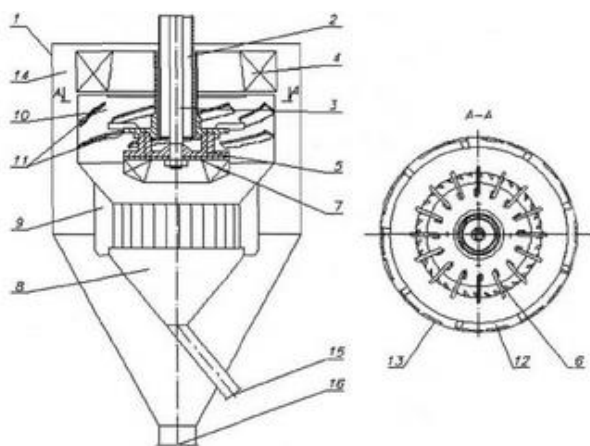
Схема динамического сепаратора: 1 – корпус; 2 – загрузочный канал; 3 – приводной вал; 4 – вентилятор; 5 – распределительное устройство; 6 – контролопасти; 7 – крыльчатка; 8 – камера осаждения крупной фракции; 9 – лопасти; 10 – сепарационная камера; 11 – устройство; 12 – многозаходные ленты; 13 – канал отвода материала; 14 – камеры осаждения мелкой фракции; 15, 16 – разгрузочный канал крупной и мелкой фракции соответственно
